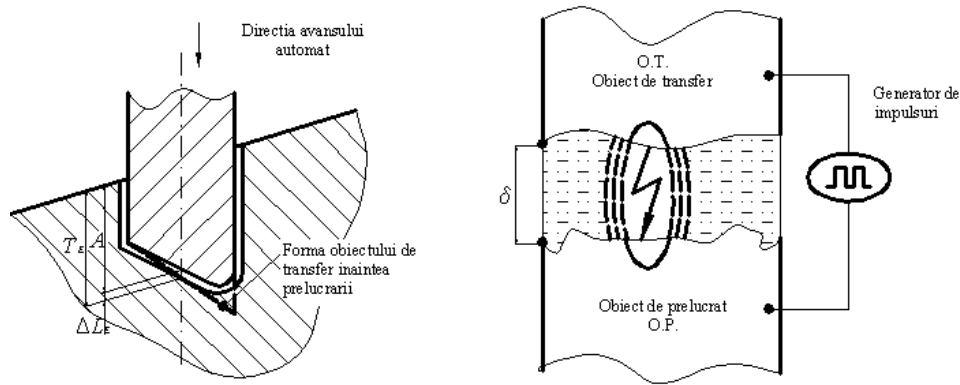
Schema de principiu a prelucrării dimensionale prin eroziune electrică.
